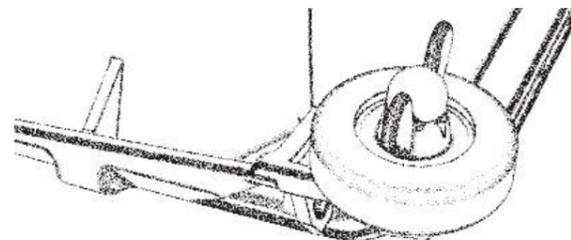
Schéma d'achèvement de l'installation de la poulie gauche
